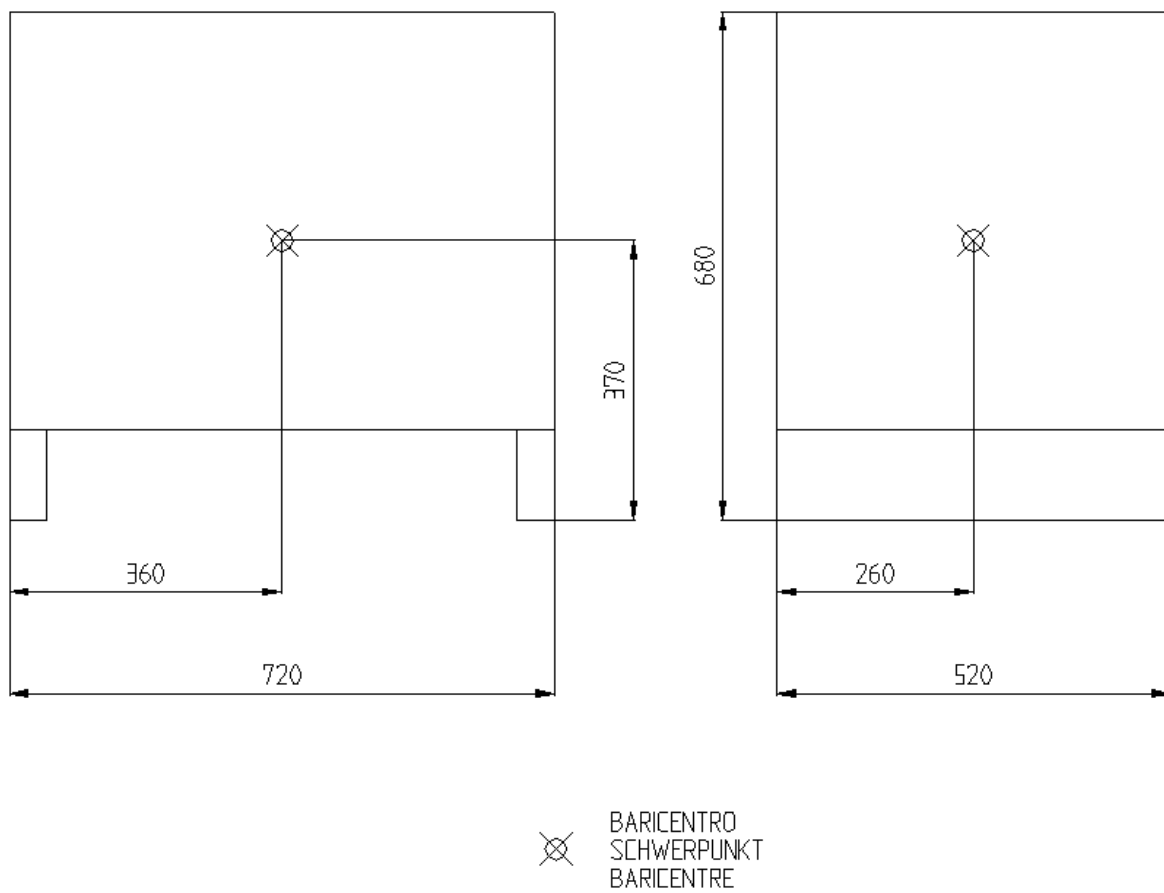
Упакованный инструмент. Габаритные размеры и центр тяжести
